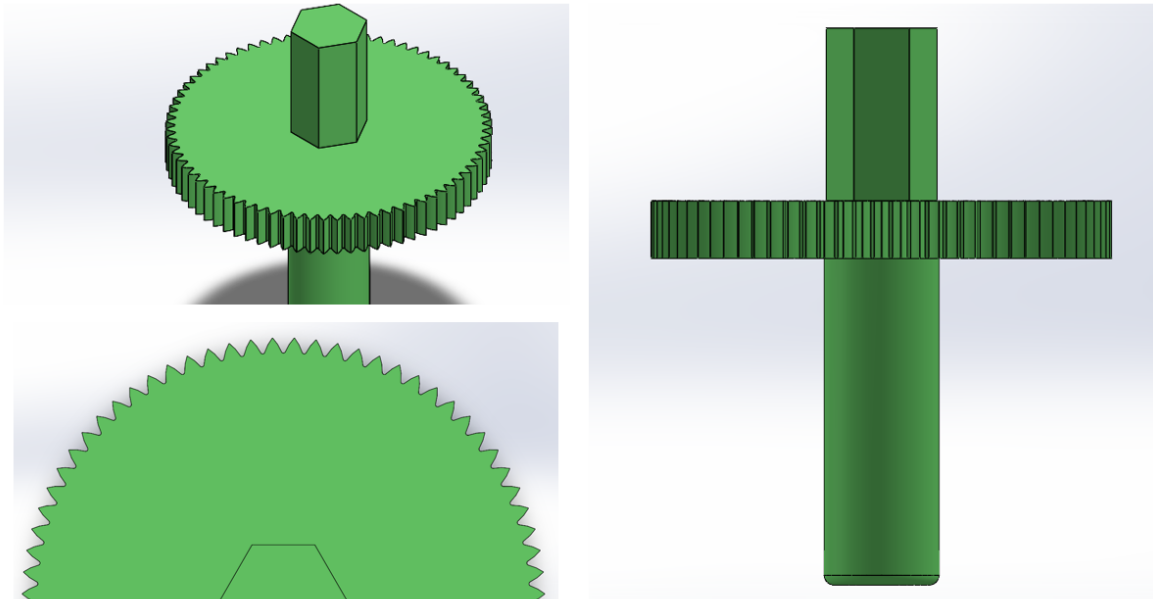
Engranaje reductor con eje hexagonal, realizado con SolidWorks
